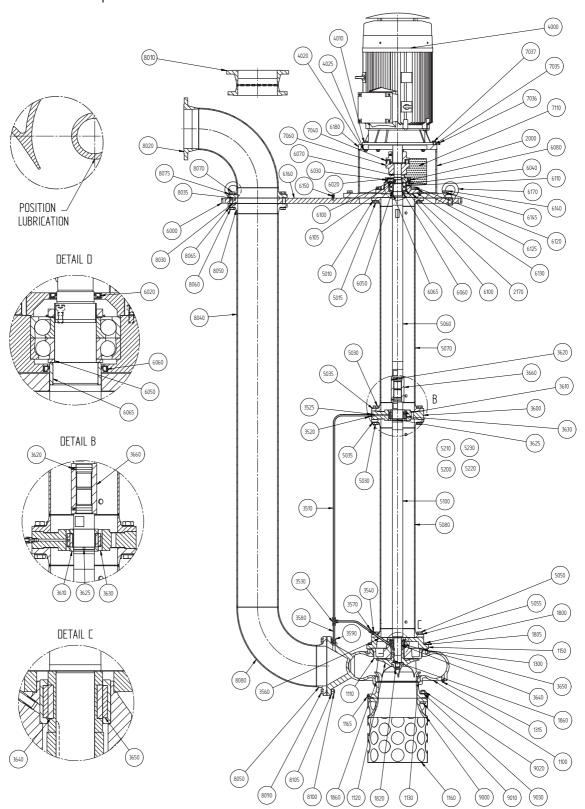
Pompe avec groupe d'étanchéité d'arbre S0, groupe de palier 4.
